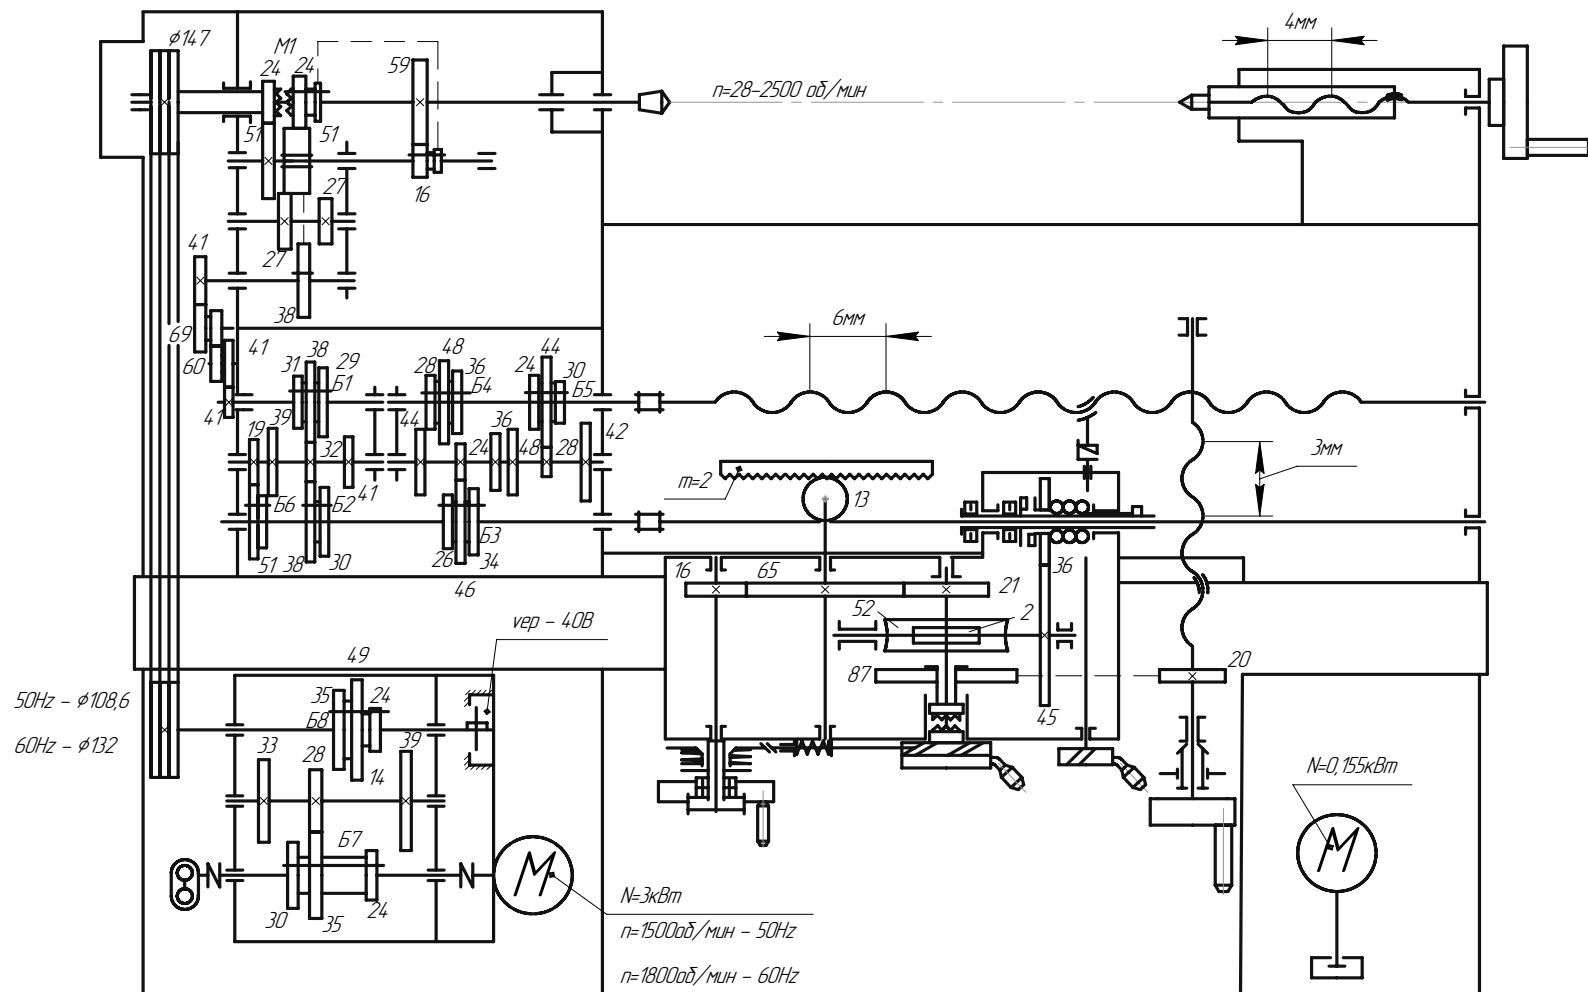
Кинематическая схема токарно-винторезного станка TUM-35
